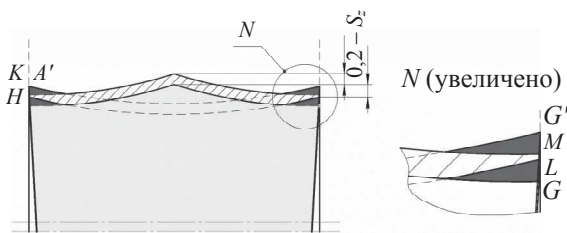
Схема формирования пропила дисковой твердосплавной пилой с плоско-треугольным профилем зубьев
